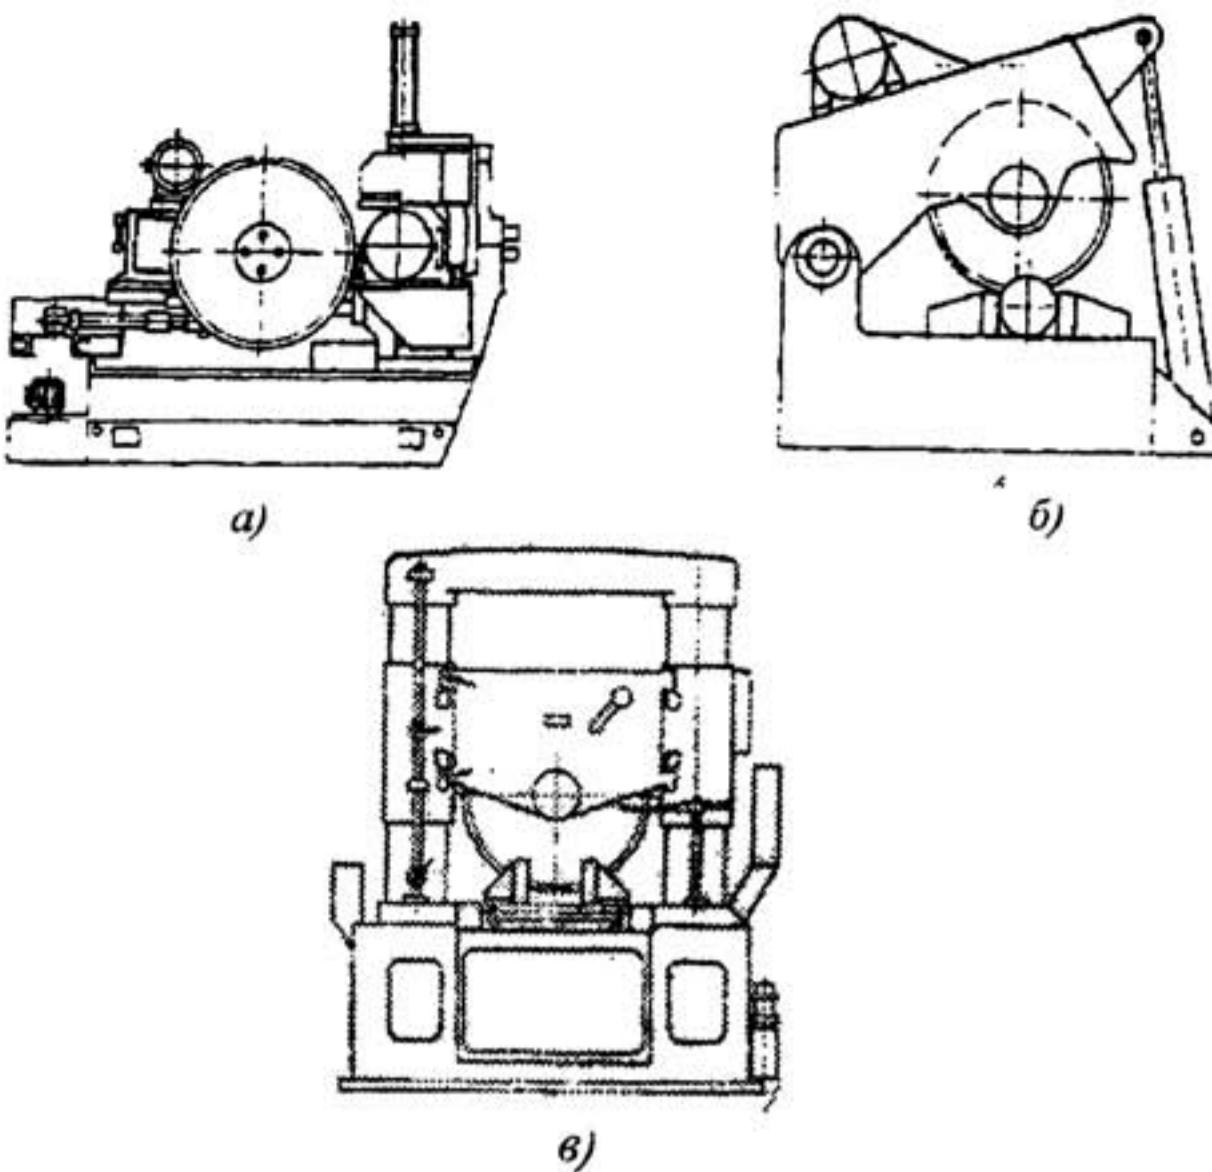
Станки для холодного разрезания металла дисковыми пилами с горизонтальным (а), качательным (б) и вертикальным (в) движениями подачи.
